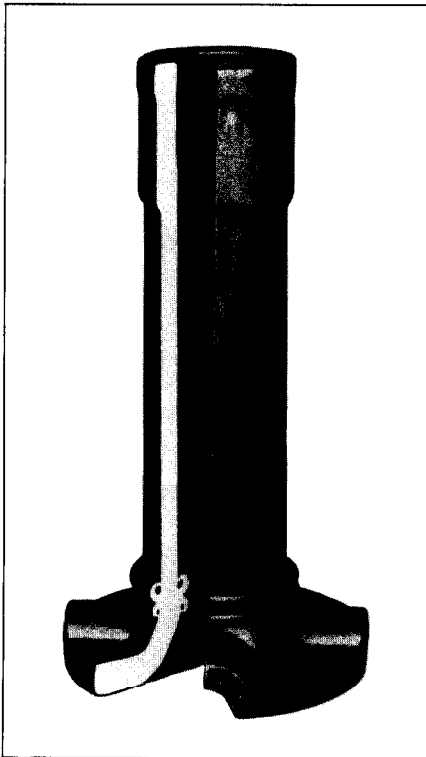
Reibschweißen: Spindel für Bodenabstützung (Stückmasse 11,8 kg, Rohraußendurchmesser 85 mm, Höhe 368 mm) aus C 35 N, Schweißquerschnitt 2840 mm²
